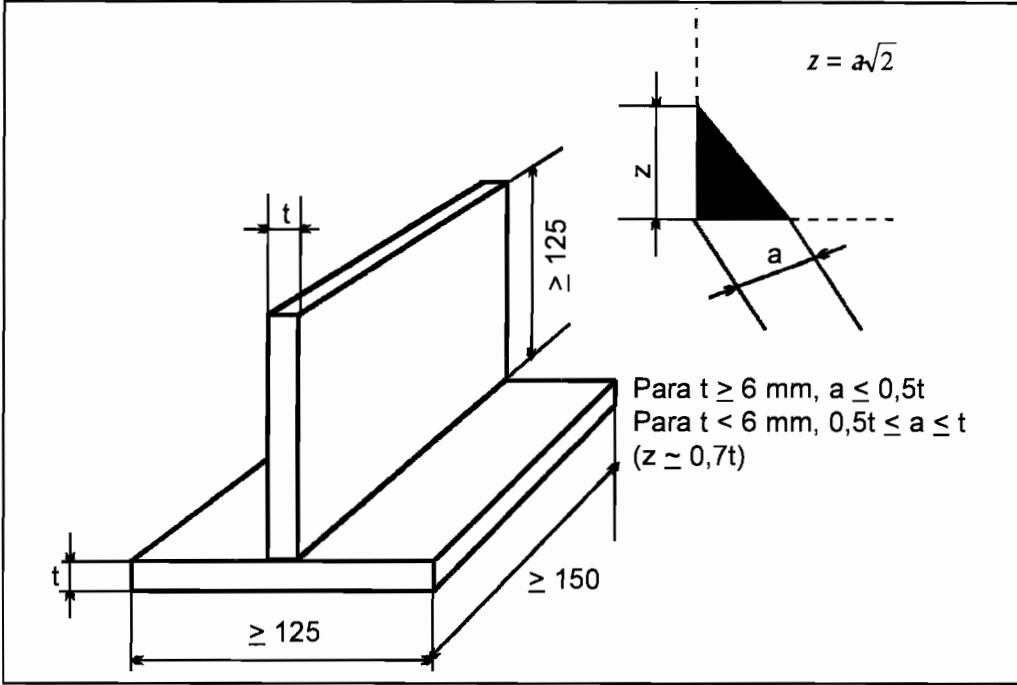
DIMENSIONES DEL CUPÓN DE PRUEBA PARA EL SOLDEO DE CHAPAS EN ANGULO (DIMENSIONES EN MILÍMETROS)
